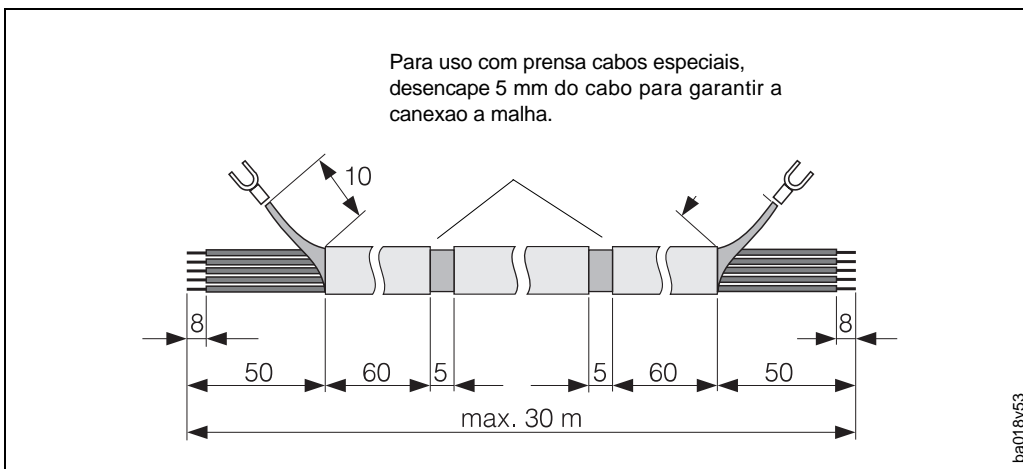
Instrucoes para preparacao do cabo entre o transmissor remoto e o sensor
